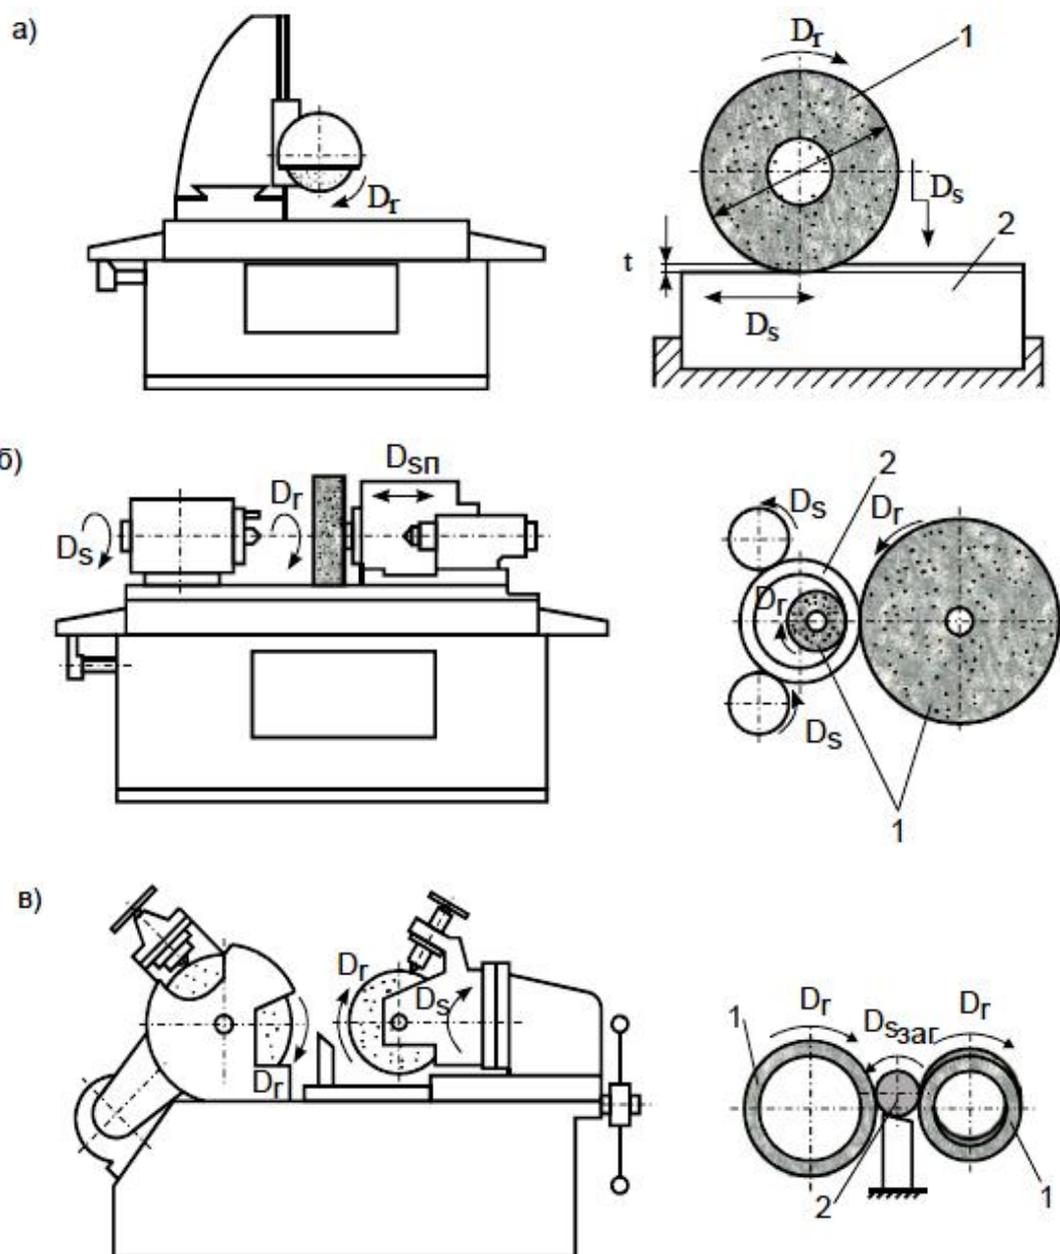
Шлифовальные станки и основные виды шлифования:
